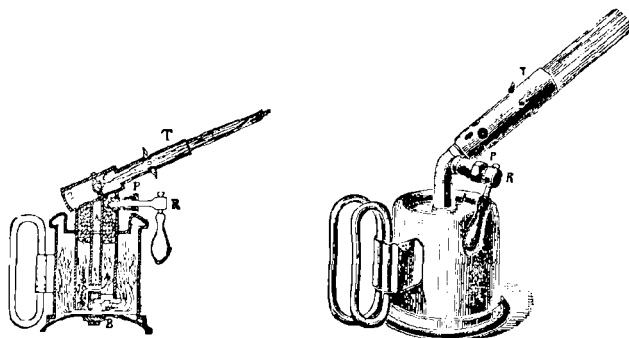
Lampe à souder « L'Inexplosible » (Longuemare).
